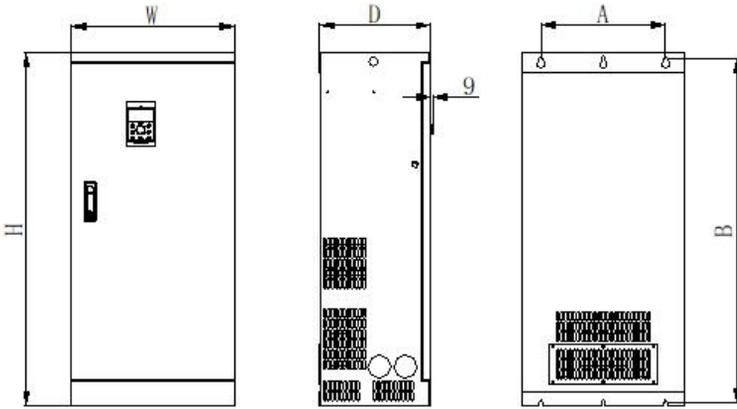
380V (4T) 160~185kW变频器外型尺寸及安装尺寸示意图
